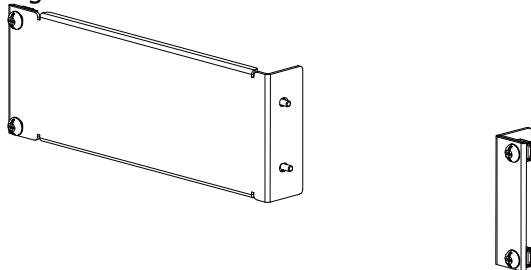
Rack Mount Kit (RM-1-DG1000Z)
